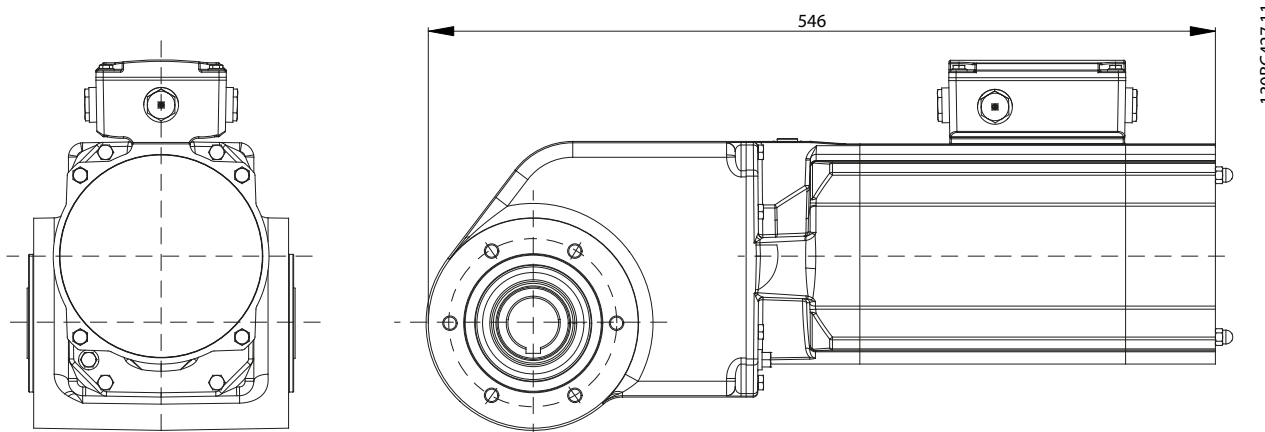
Размеры: OneGearDrive с дополнительным механическим тормозом
